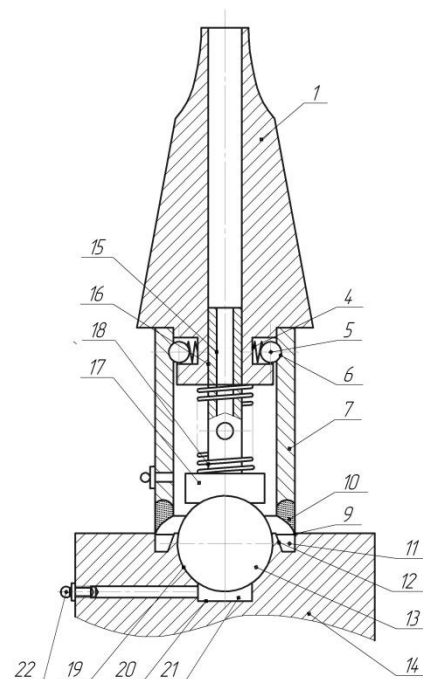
Пристрій для завальцювання кульок в корпусних деталях
